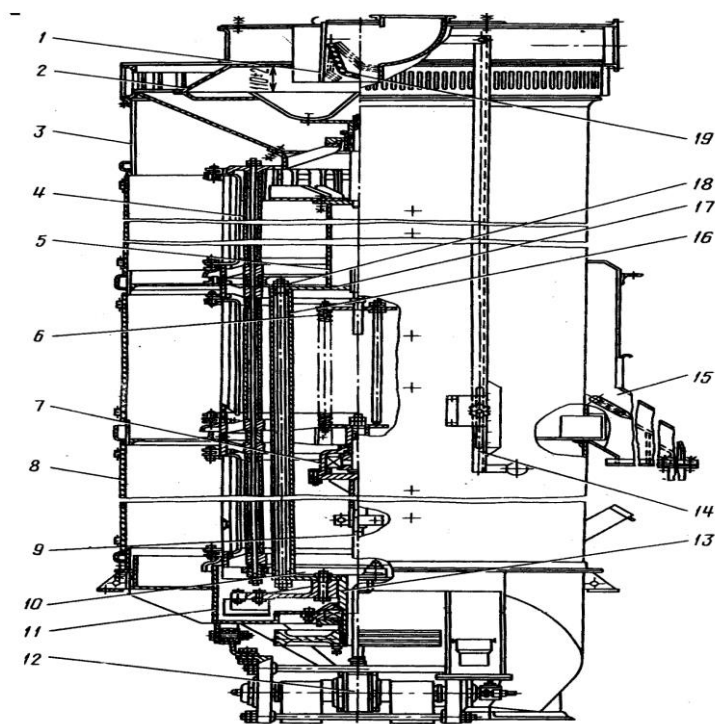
Загальний вигляд блока зерноочисного:
